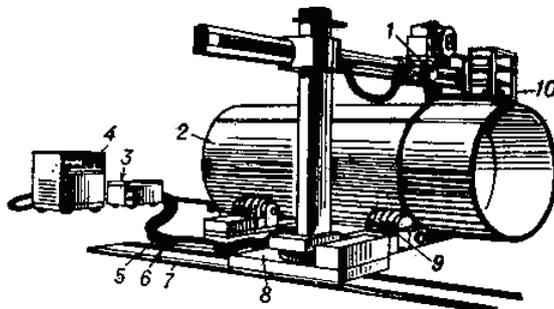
Сварочный пост для дуговой сварки:
